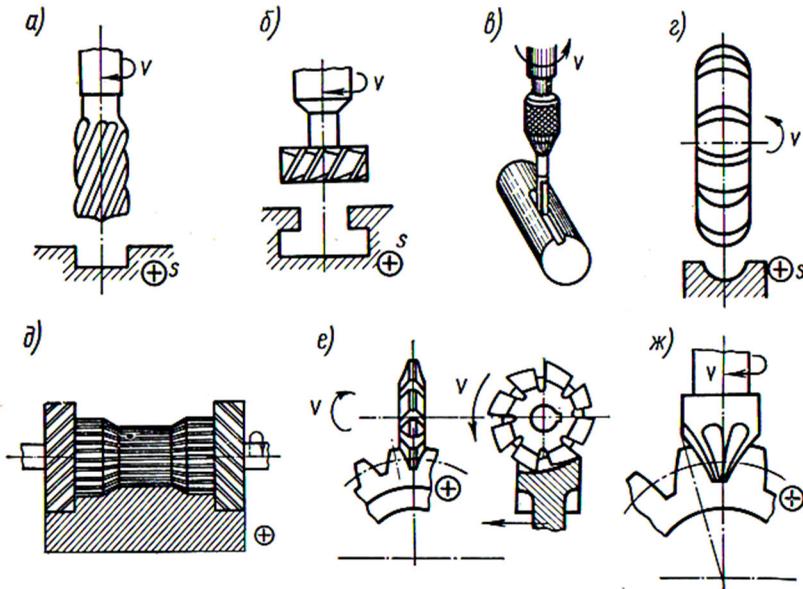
Основные виды фрезерования пазов, канавок, фасонных поверхностей и зубчатых колёс
